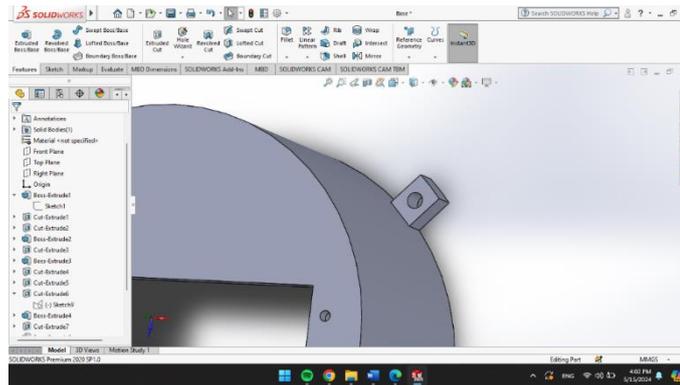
Hasil *Extruded Cut* Tempat Motor Servo
